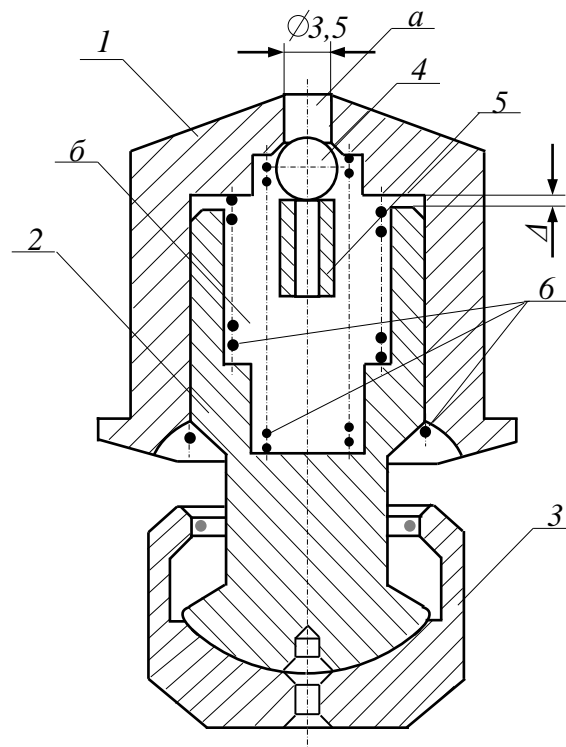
Гідроштовхач механізму газорозподілу ЕУТ Д49: 1 - втулка; 2 – штовхач; 3 – ковпачок; 4 – кульковий клапан; 5 – упор; 6 – пружини
